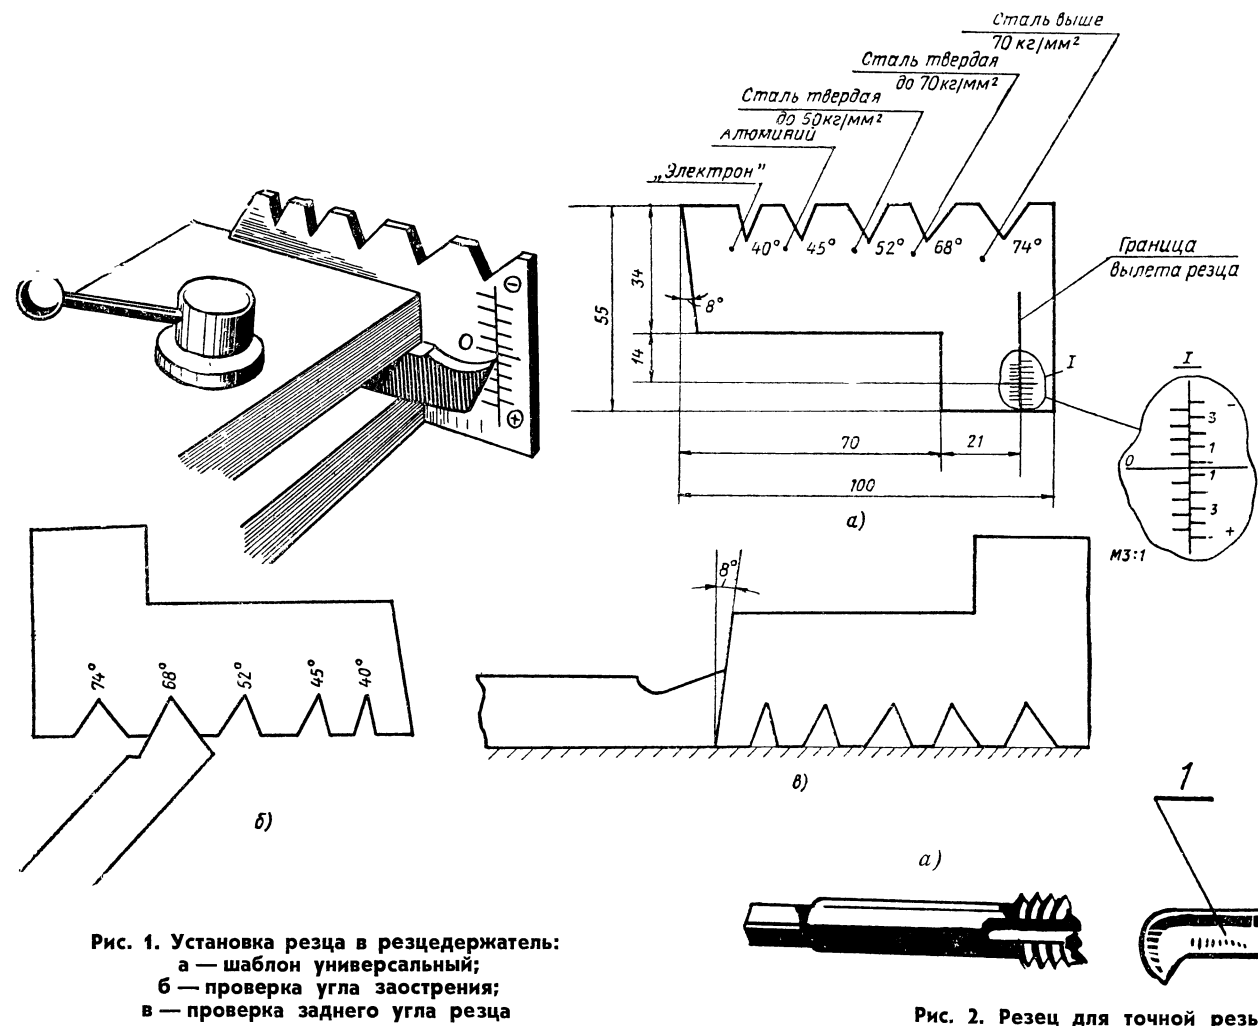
Установка резца в резцедержатель: а — шаблон универсальный; б — проверка угла заострения; в — проверка заднего угла резца
